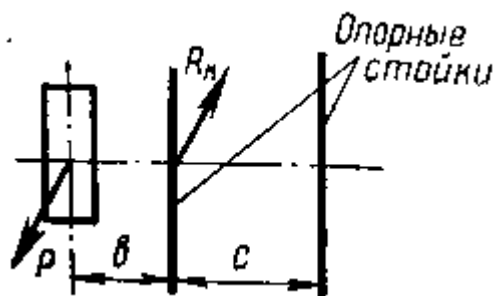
Схема сил действующих на опорно-концевые стойки
